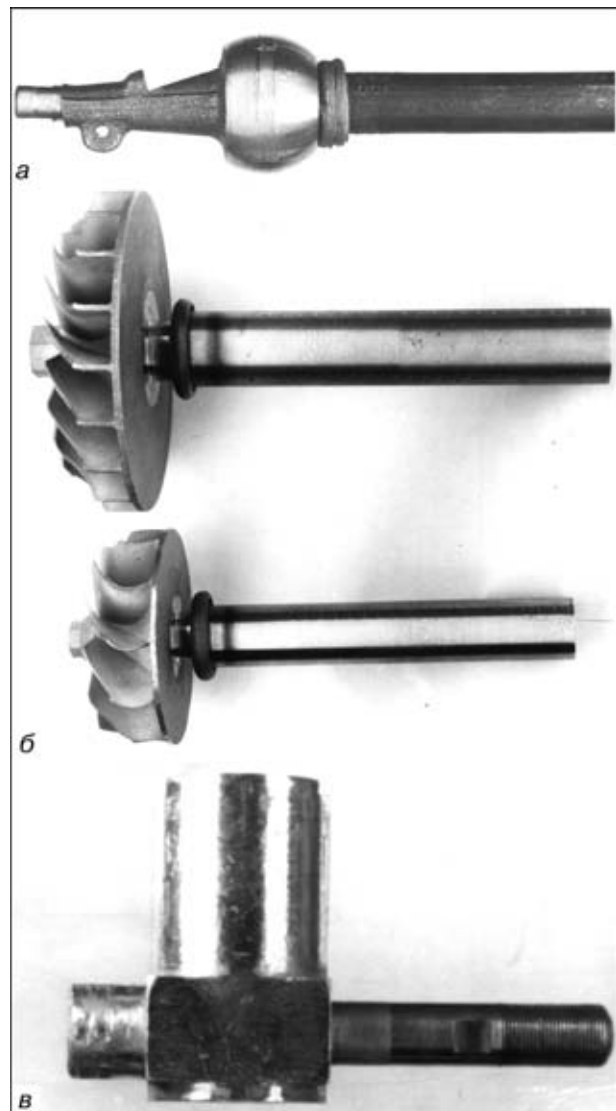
Изделия, выполненные сваркой трением с регулируемым торможением на установке СТ-120: а — рычаг коробки передач автомобиля «Москвич»; б — роторы турбокомпрессоров дизельных двигателей; в — сталеалюминиевый переходник
